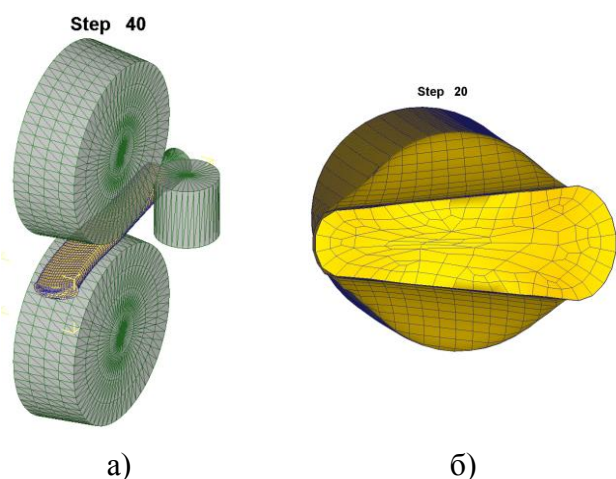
Схема вальцювання заготовки конічними валками а) та форма поперечного перетину вальцьованої ділянки б)
